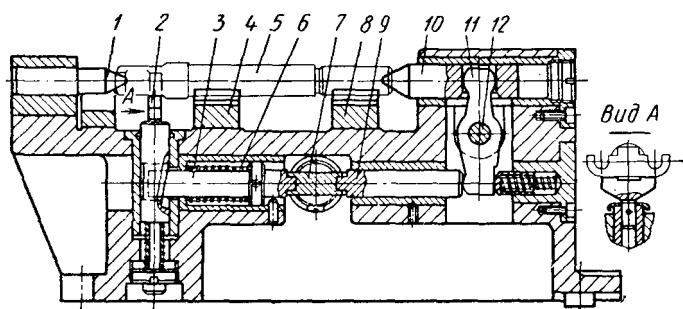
Фрезерное приспособление с механизированной дополнительной опорой
